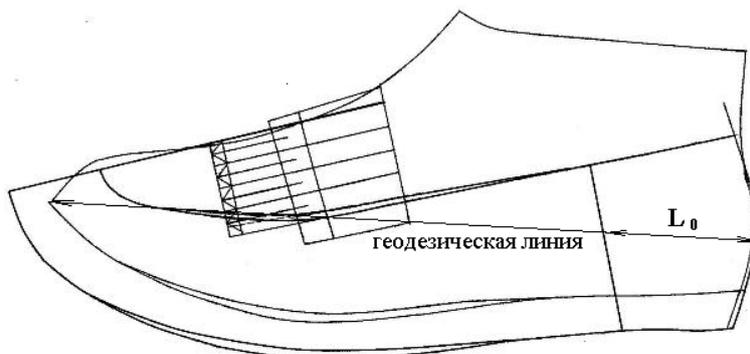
Схема замера длинотных параметров деталей заготовки
